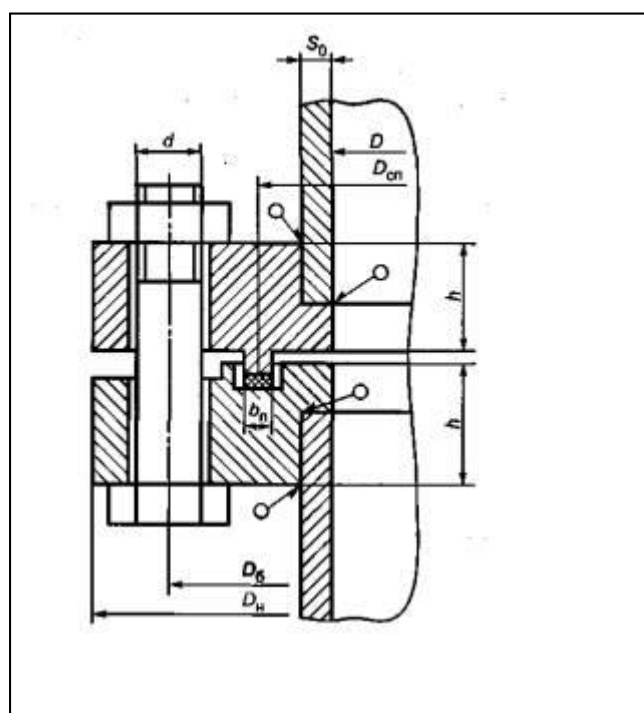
Фланец корпуса и рубашки аппарата
